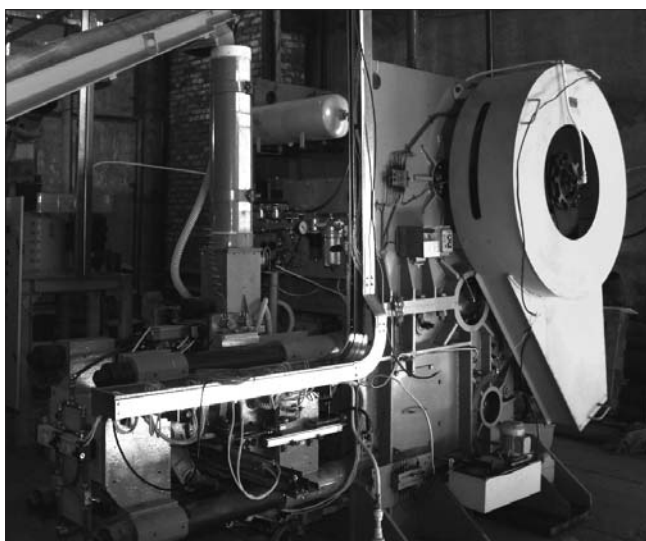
Пресс полусухого прессования ШЛ 403Б
